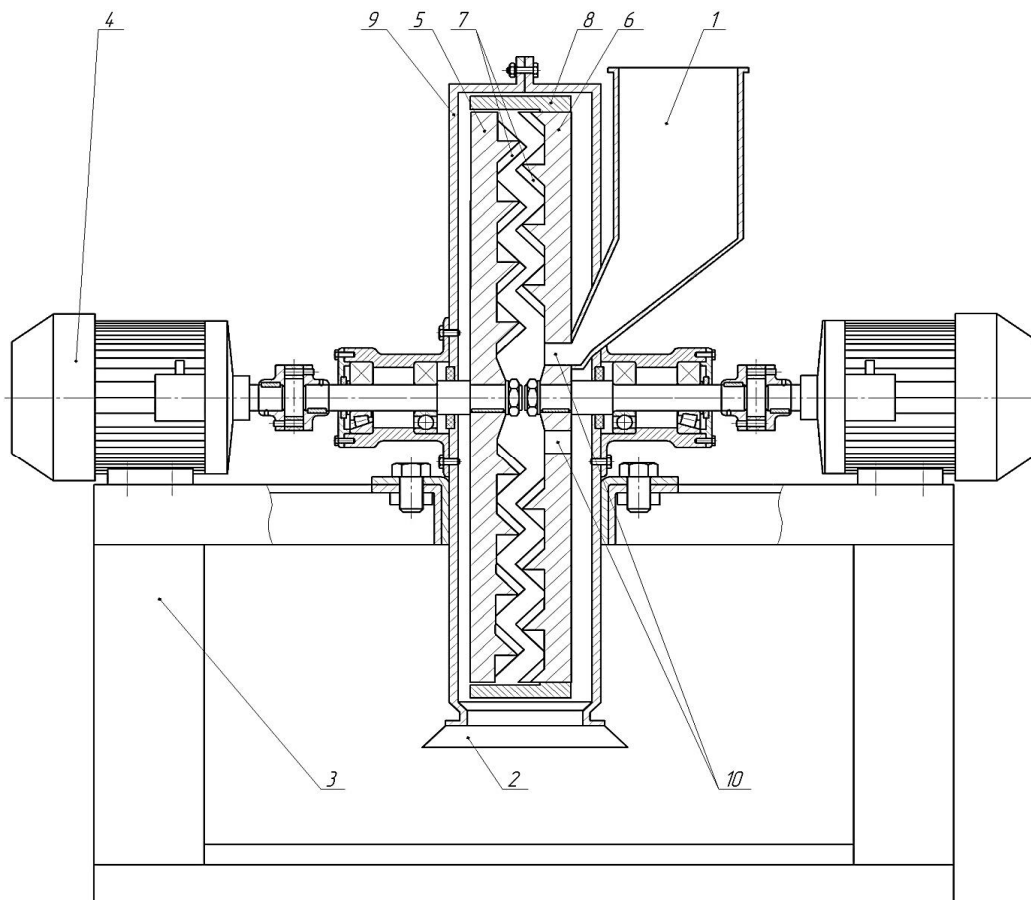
Ударно-центробежная дробилка: 1 – бункер; 2 – выгрузное устройство; 3 – рама; 4 – электродвигатель; 5 – отбойный диск; 6 – загрузочный диск; 7 – ножи; 8 – лопатка; 9 – корпус измельчителя; 10 – загрузочные окна
